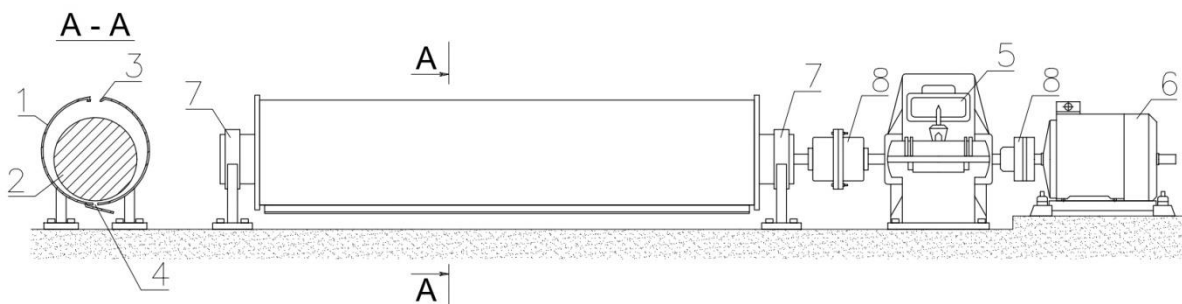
Схема несоосного универсального размалывающего устройства.
